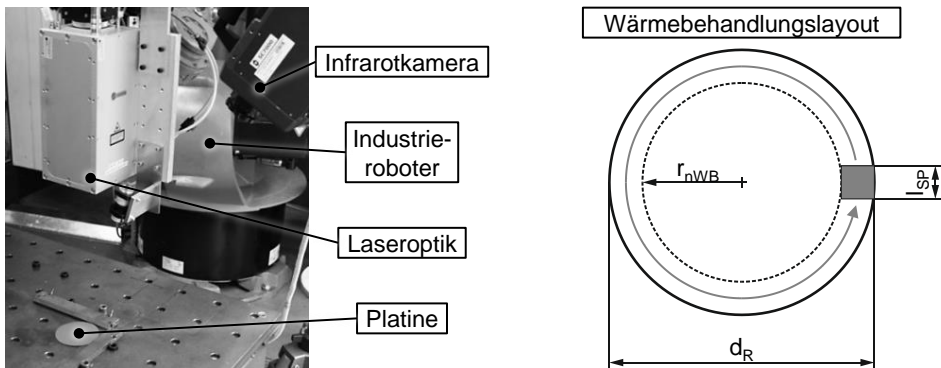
Versuchsaufbau Laserwärmebehandlung mit Layout
